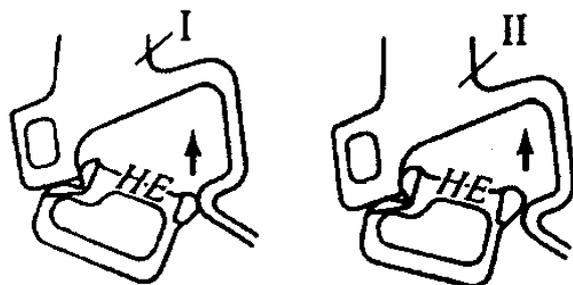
Проверка ширины зева корпуса автосцепки шаблоном 821 р-1
